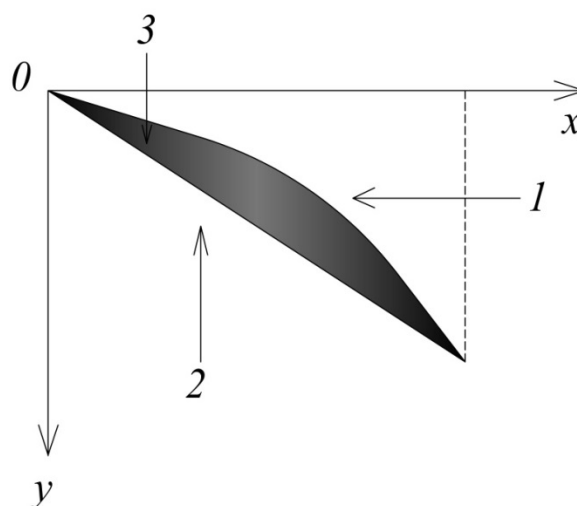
Схема удаления металла с головки рельса по предполагаемой технологии: 1 – шлифовальный круг; 2 – обрабатываемый рельс; В – полоса шлифования металла
